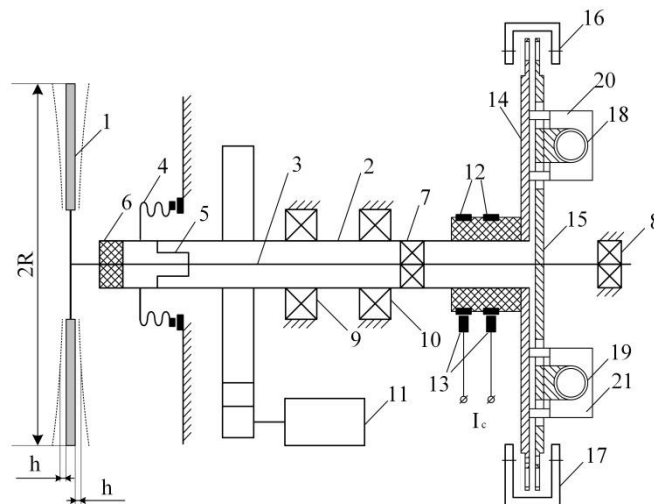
Конструкція механічної частини ротаційного вимірювача концентрації паперової пульпи з магнітоелектричною компенсацією моменту в'язкісного тертя. 1 - чутливий елемент дископодібної форми; 2 – основний порожнистий вал приладу; 3 – вал чутливого елемента; 4 – ущільнення основного порожнистого вала з сільфона і кільцевих вставок зі сплаву карбід вольфраму-кобальт; 5 – гнучке ущільнення з повздовжньо гофрованої тонкостінної трубки; 6 – еластичне ущільнення для захисту від забивання ущільнення 5; 7, 8 – підшипники вала чутливого елемента; 9, 10 – підшипники основного порожнистого вала; 11 – двигун з живленням від частотного перетворювача; 12 – струмопідвідні кільця; 13 – графітокомпозитні щітки; 14 – диск з прорізами на основному валу приладу; 15 – диск з прорізами на валу чутливого елемента; 16 – оптопара з відкритим оптичним каналом для вимірювання зміщення дисків 14 і 15; 17 – оптопара з відкритим оптичним каналом для фіксації початку відліку; 18, 19 – навитки магнітоелектричного перетворювача, які закріплені на диску 15; 20, 21 – магнітні системи, які закріплені на диску 14.
